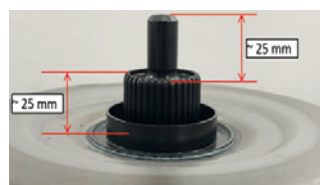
Dimensioni modificate degli ingranaggi e del perno di guida
